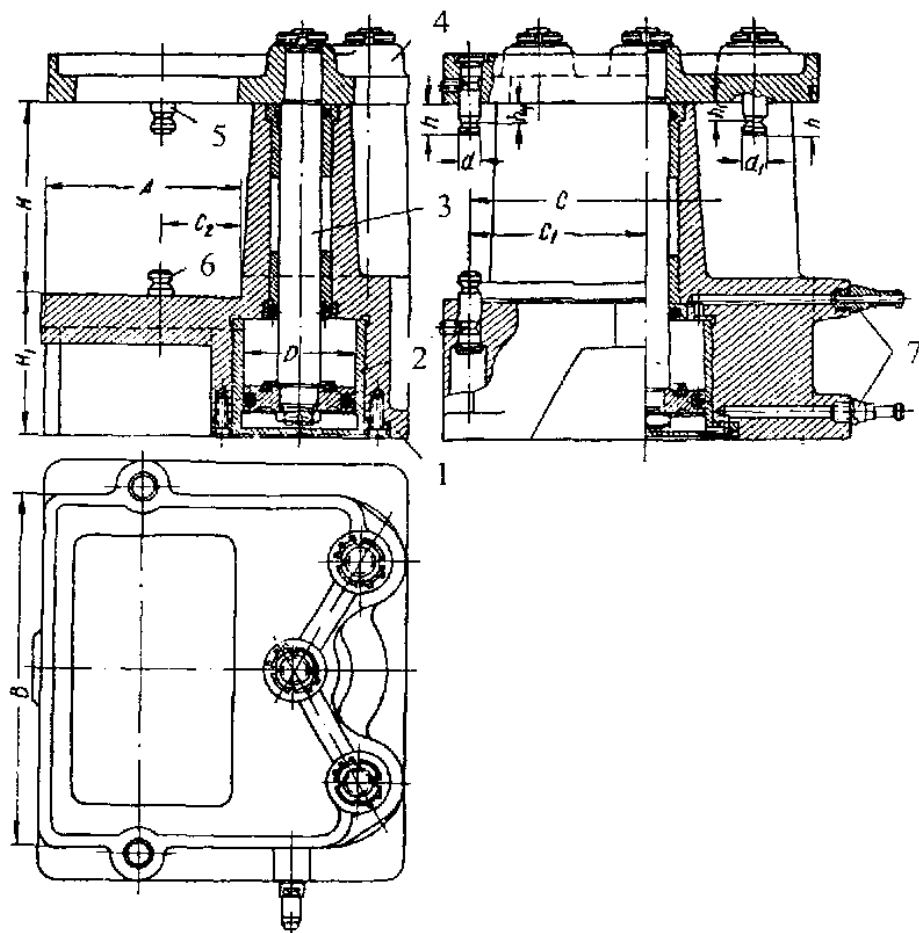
Скальчастий кондуктор консольного типу з пневматичним приводом
